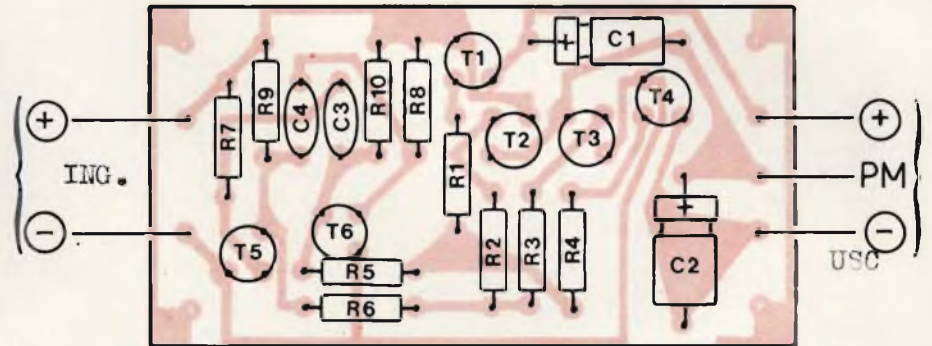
Circuito stampato del moltiplicatore di tensione visto dal lato componenti.
